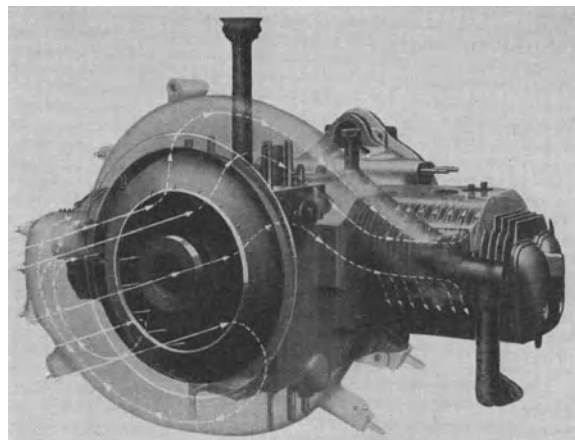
Luftgekühlter Boxermotor mit vor dem Motor liegendem Kühlluftgebläse (Neue Röhre-AG.).
